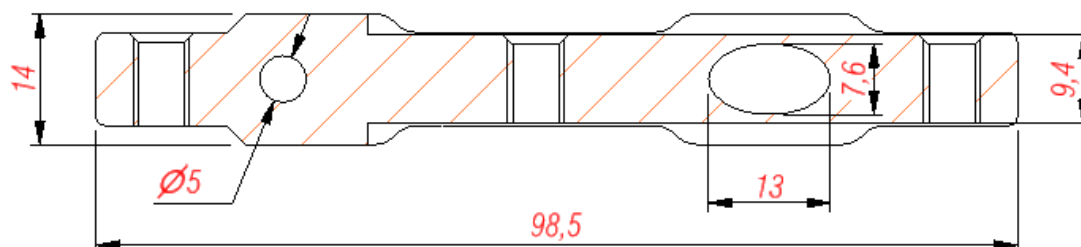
Esboço da seção transversal da câmara para o Ondulador Apple 2.
